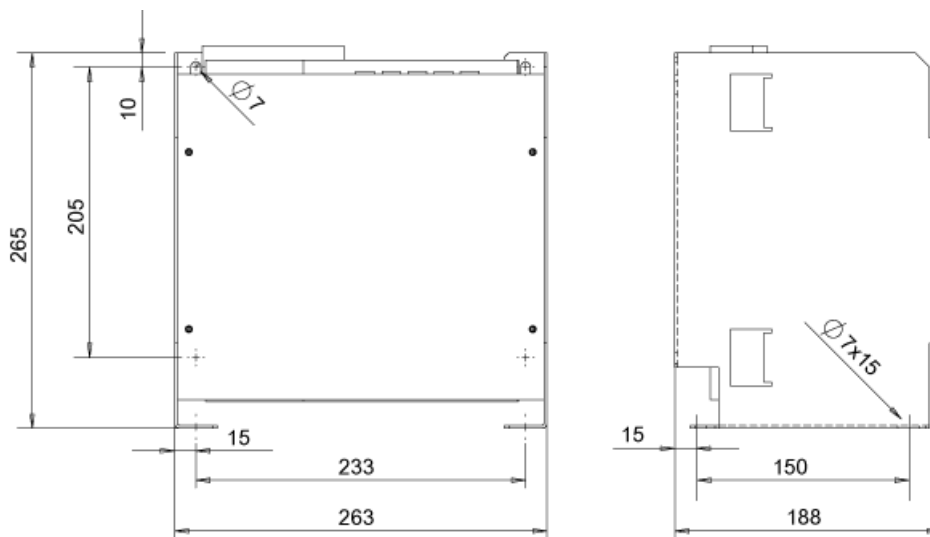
Габаритный чертеж схемы ограничения напряжения, тип 1
